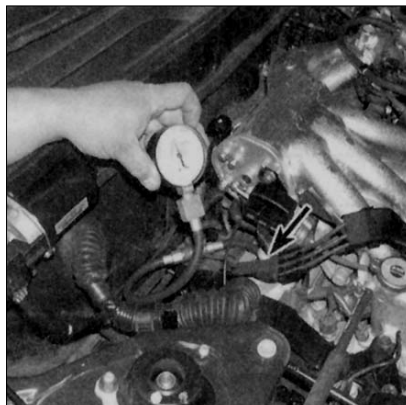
Для определения ВМТ на шестицилиндровых V-образных двигателях можно использовать компрессионный манометр в отверстии свечи зажигания № 1
